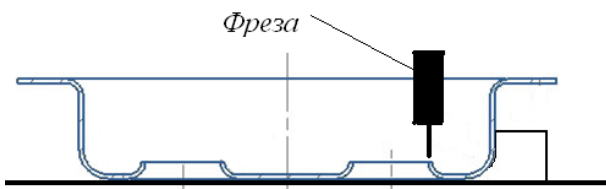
Схема размещения заготовки на столе фрезерного станка
